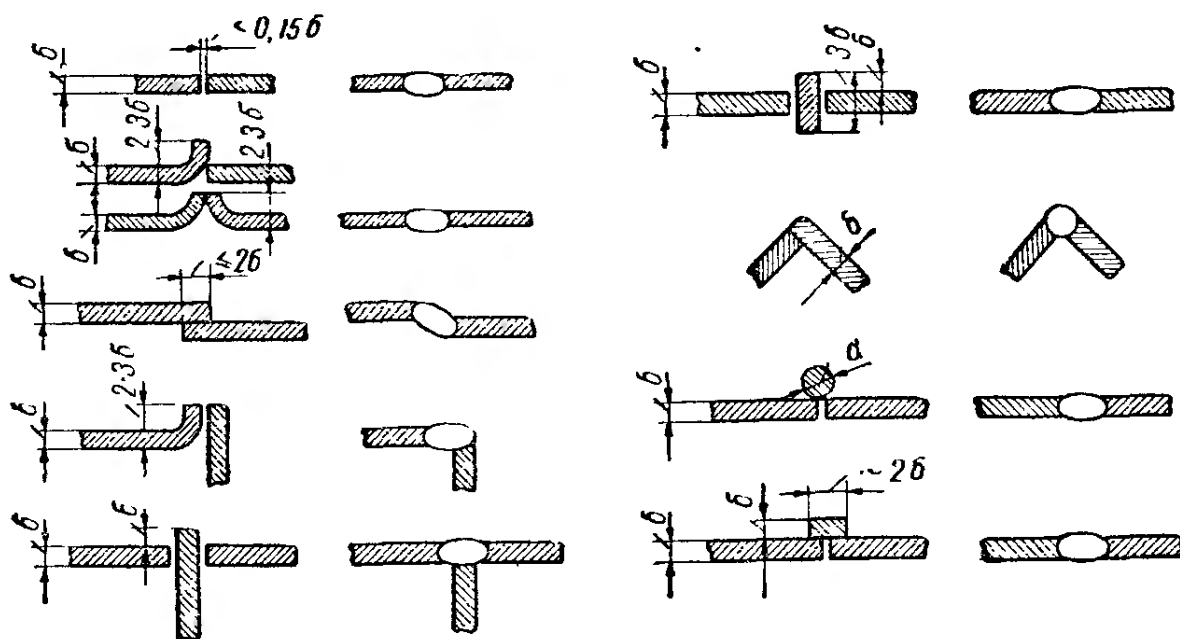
Типы соединений, применяемых при аргоно-дуговой сварке тонколистового металла
